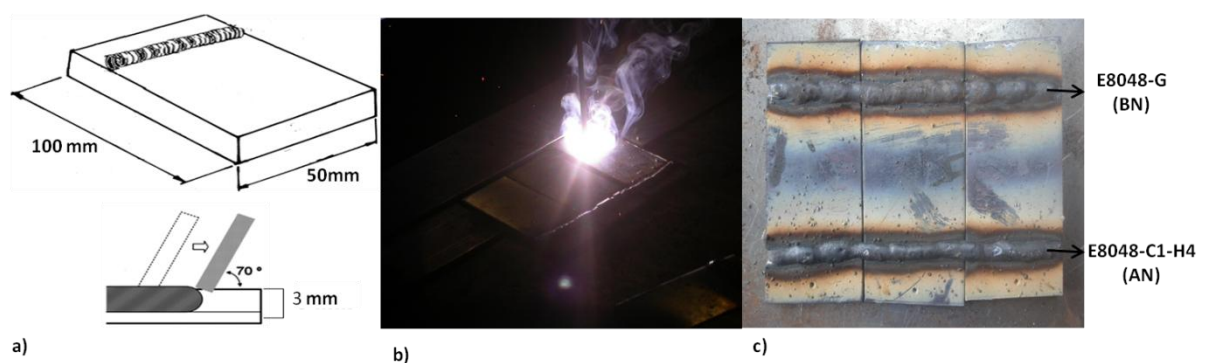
Esquema de soldadura y posición del electrodo utilizando electrodos tipo BN y AN: (a) Esquema del ángulo de posición de soldeo y dimensiones de la chapa de acero, (b) proceso de soldeo y (c) aspecto de las probetas, ya con los cordones de soldadura, una vez finalizado el proceso de soldeo.
